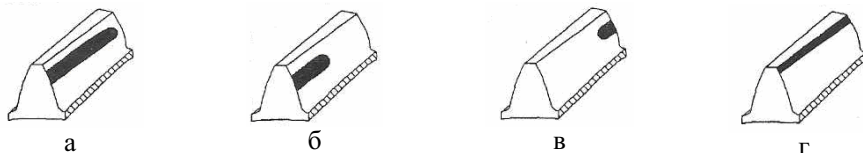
Контроль качества сборки при регулировании зацепления зубцов конической зубчатой передачи с помощью краски:
